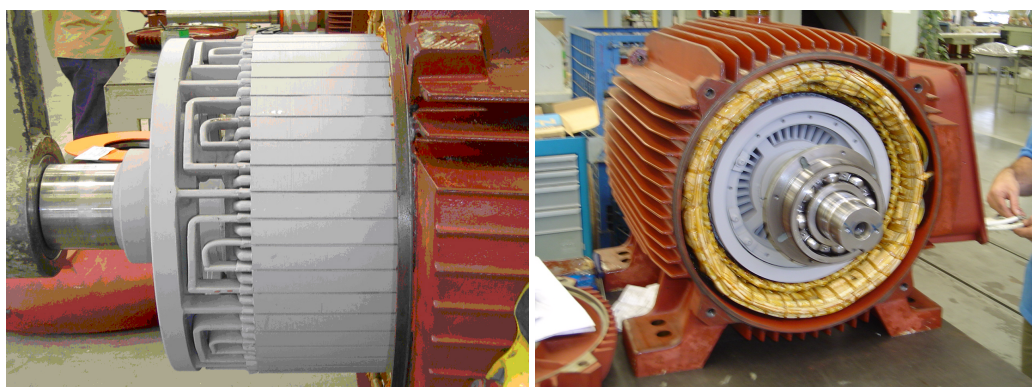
(a) Rotor, (b) Carcaça.
